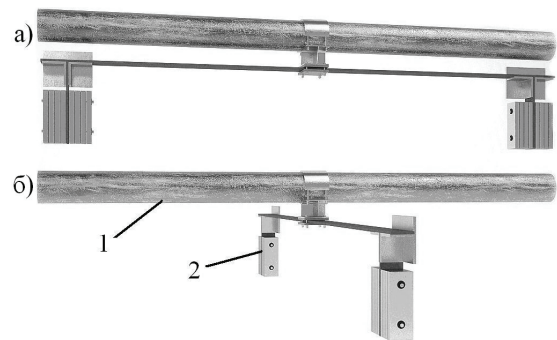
Конструкция пластинчато-балочного виброударного ДГК: а – расположение ДГК вдоль шины; б – расположение ДГК поперек шины; 1 – шина; 2 – ДГК.
